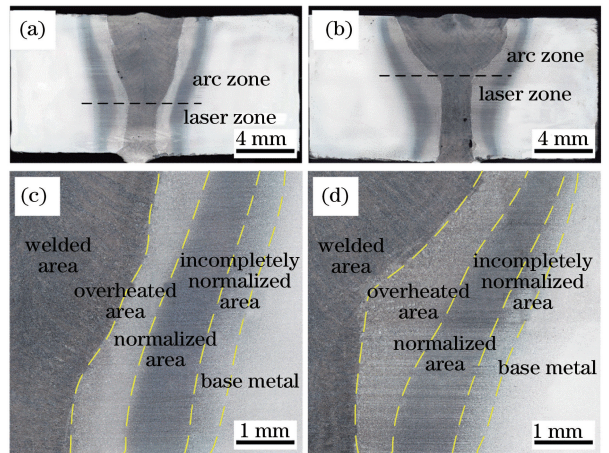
焊接接头横截面形貌。(a)电弧先导,宏观形貌;
